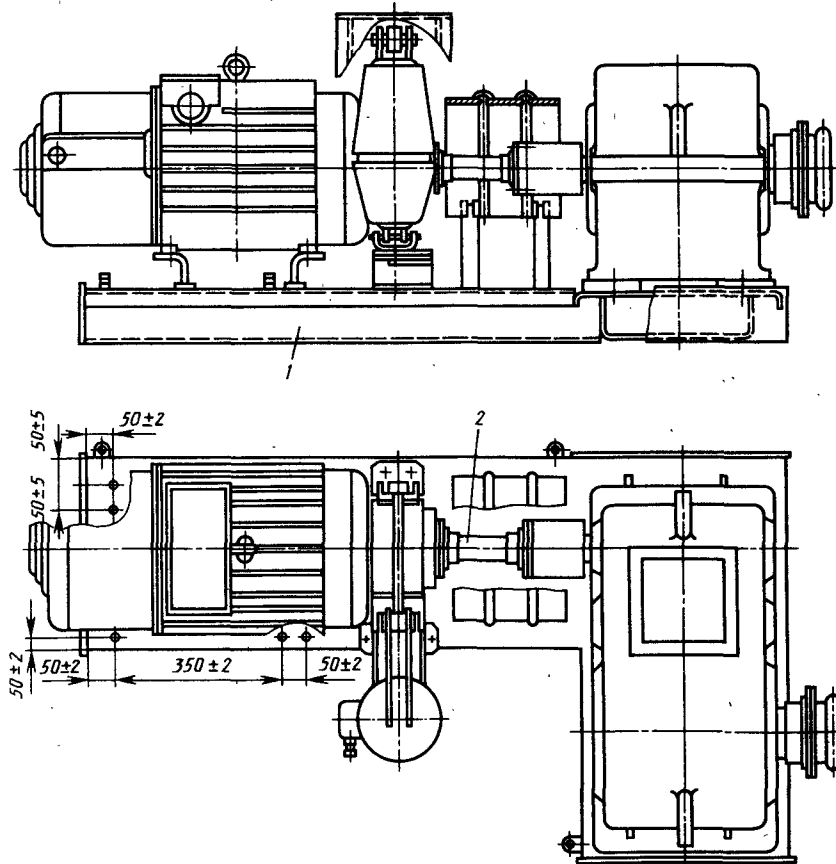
Привод механизма передвижения с горизонтальным редуктором
